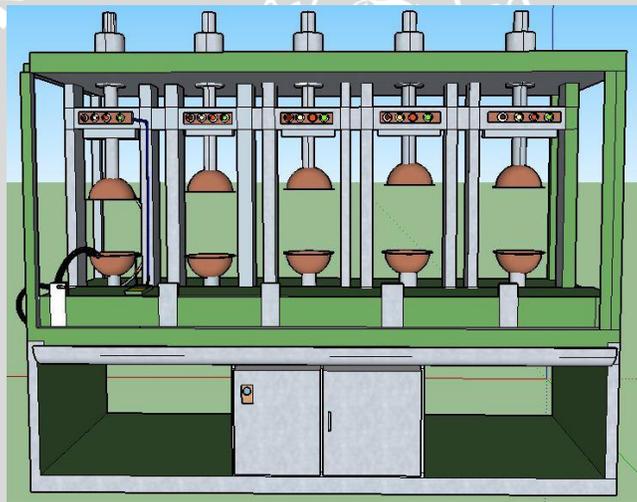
Rekomendasi Rak Susun Tampak Belakang
